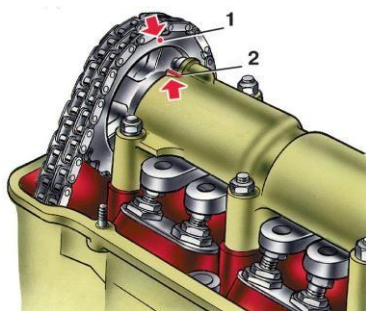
Установка поршня первого цилиндра в ВМТ на такте сжатия для регулировки клапанов: 1 – установочная метка на звездочке распределительного вала; 2 – установочный прилив на корпусе подшипников распределительного вала
